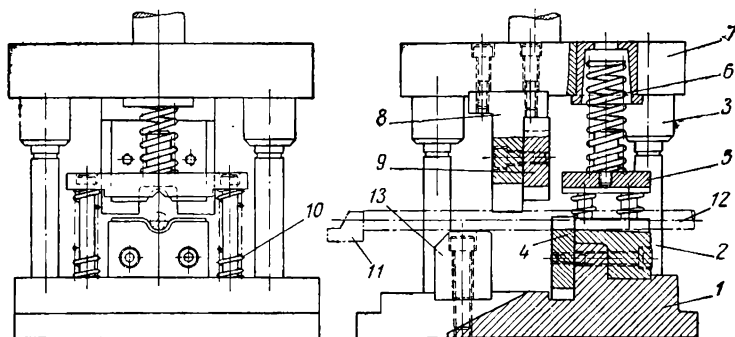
Одноопорный штамп для резки заготовок диаметром до 40 мм на кривошипном прессе: 1 — нижняя плита; 2 — направляющая колонка; 3 — направляющая втулка; 4 — нижний нож; 5 — прижимная колодка; 6 — пружина прижима; 7 — верхняя плита; 8 — державка верхнего ножа; 9 — верхний нож; 10 — возвратная пружина прижима; 11 — упор; 12 — пруток; 13 — противоприжим
